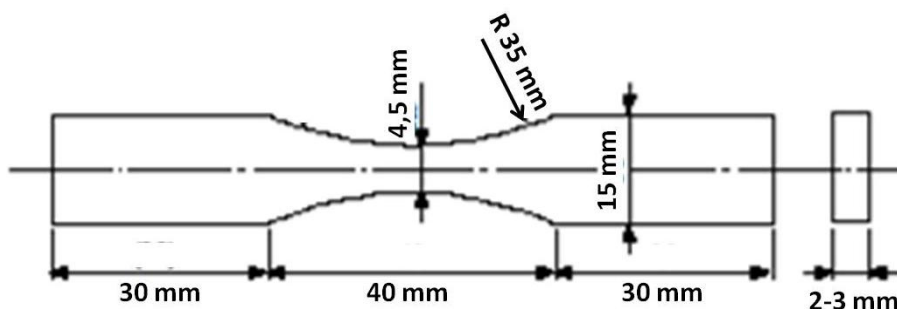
Dimensiones de las probetas de fatiga uniaxial
